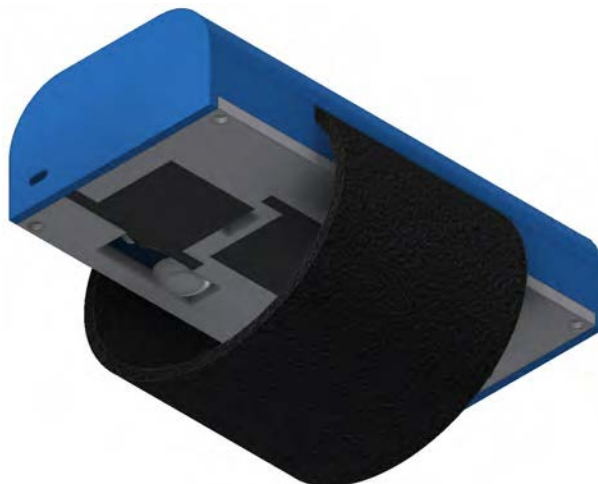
Vista inferior dispositivo de sistema de retroalimentación.
